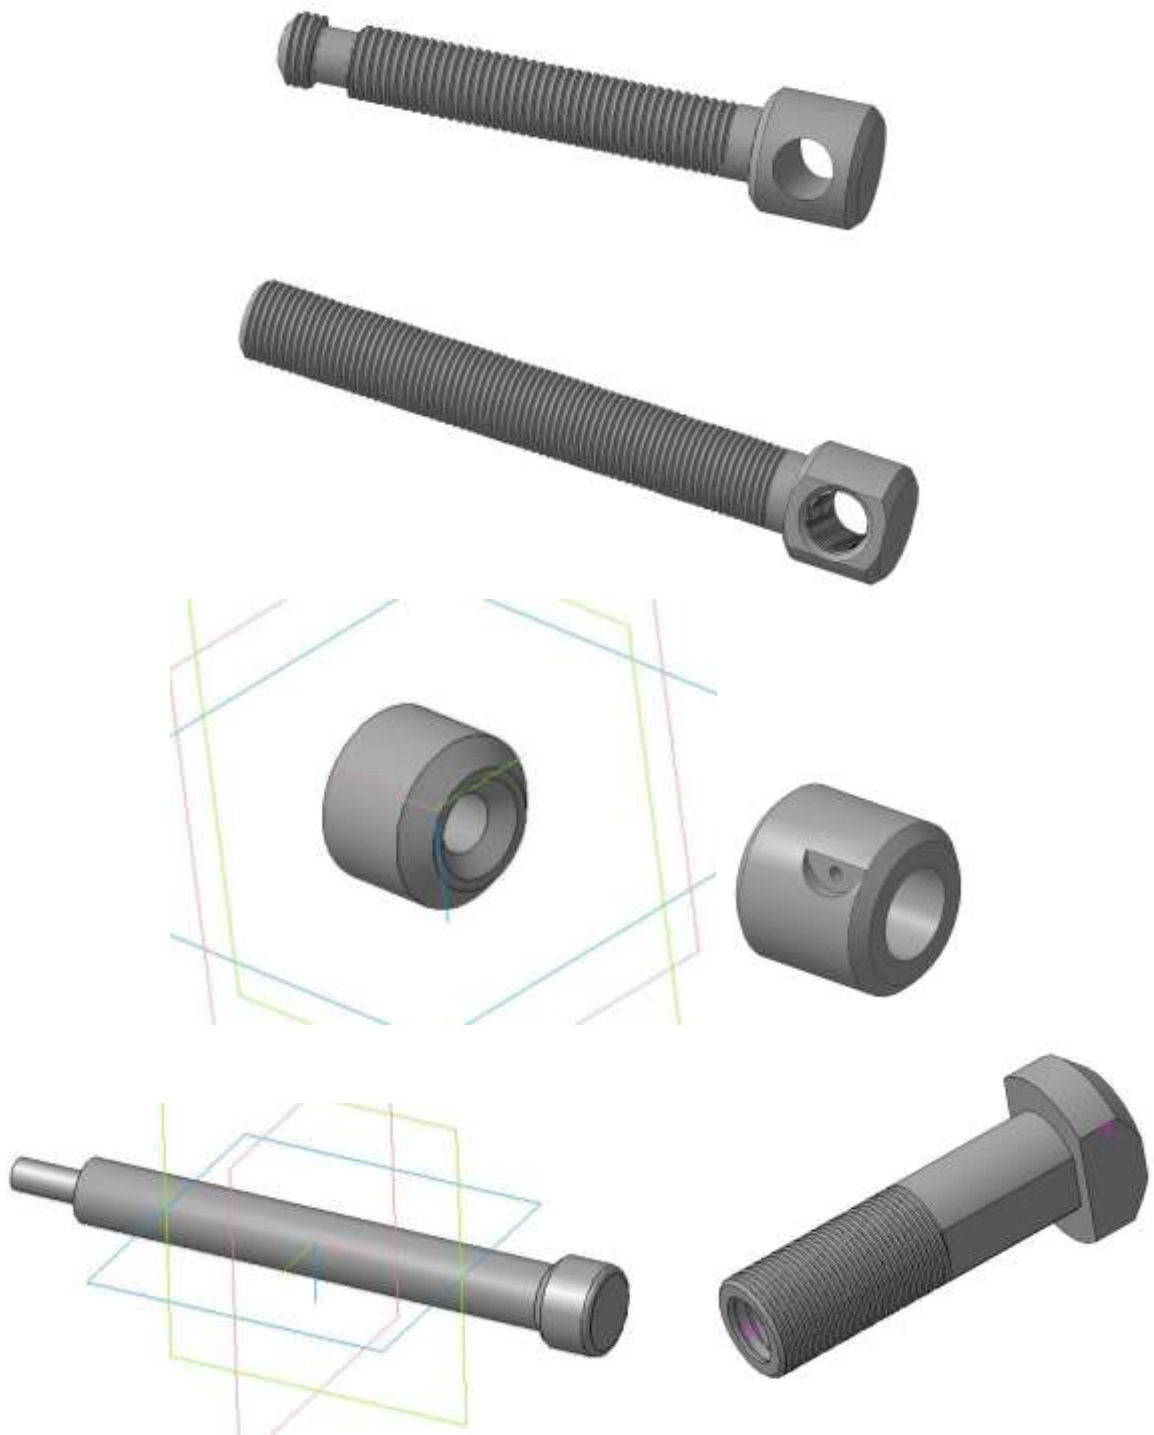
Прижим боковой, детализовка 3D сборки
